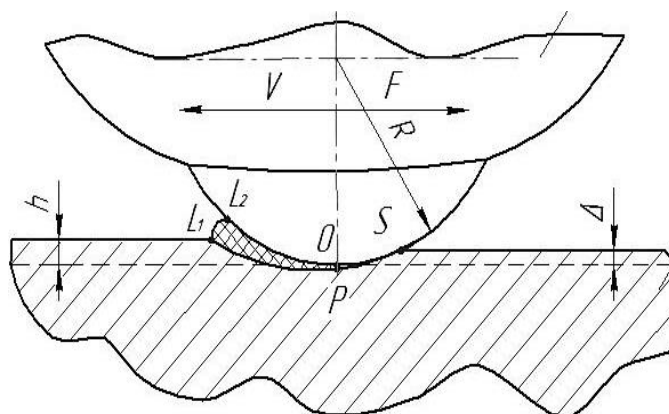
Схема контакта шарового индентора с поверхностью детали при алмазном выглаживании [4]
